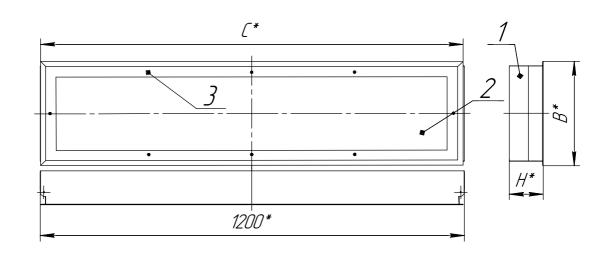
1. Корпус в сборе, 2. Обечайка в сборе. 3. Винт
